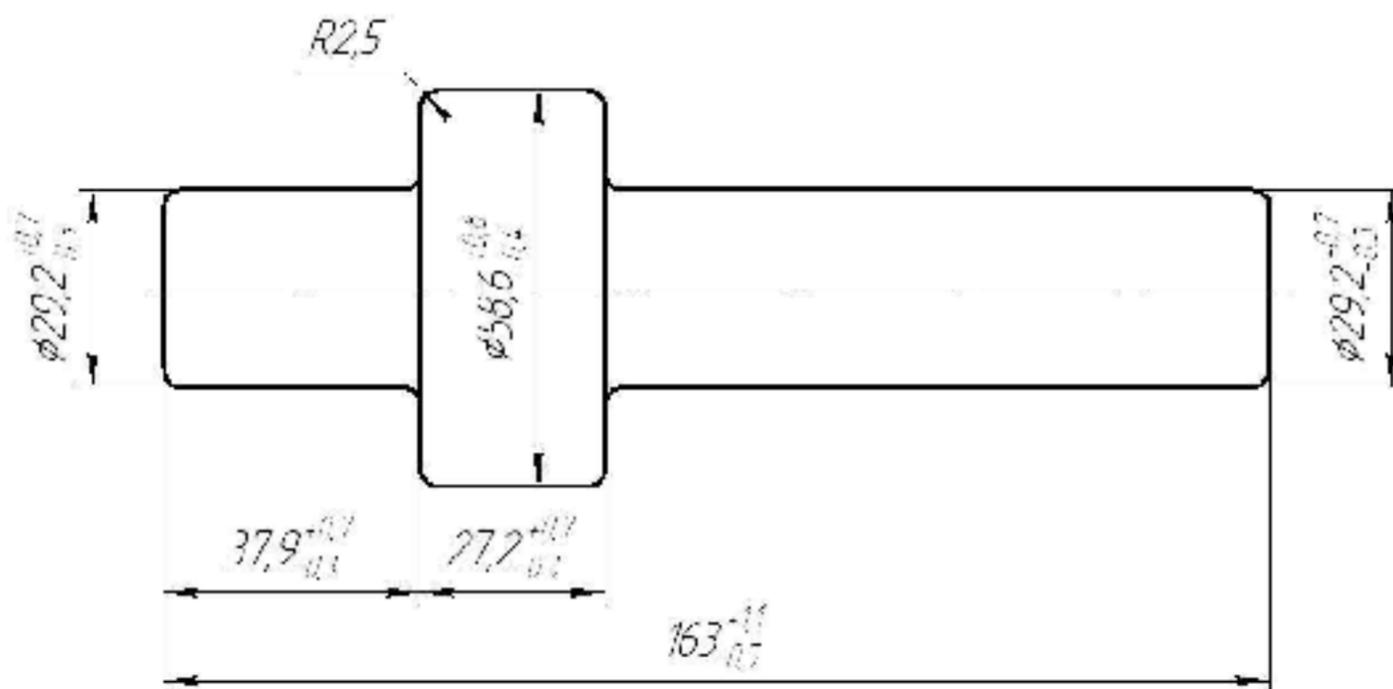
Ескіз заготовки при штампуванні на КГШП (3)
